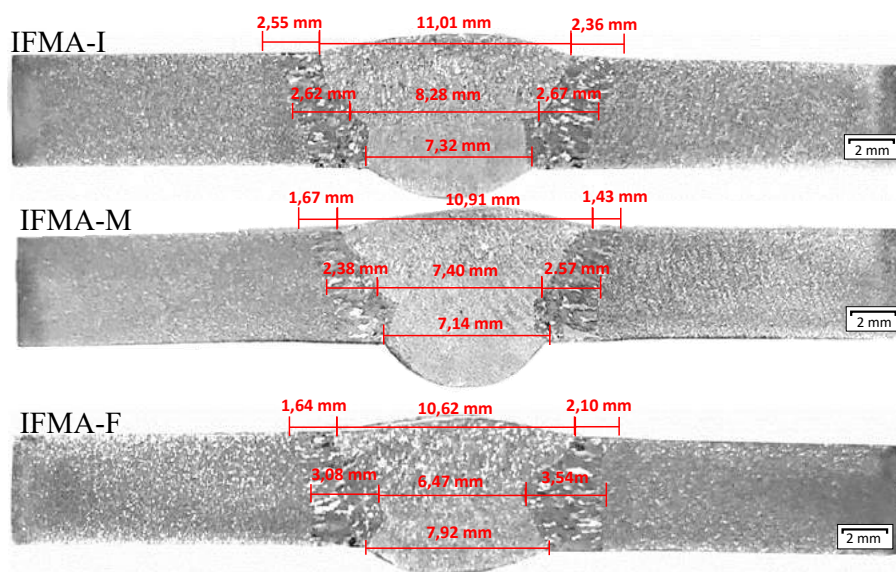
Dimensões das regiões de soldagem das amostras IFMA.
